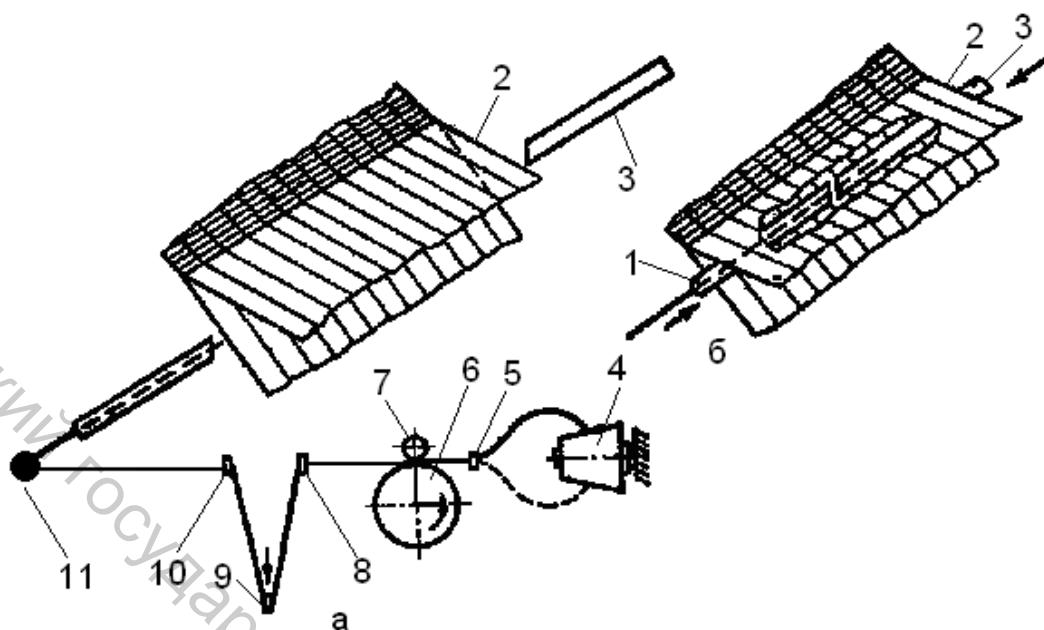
Схема прокладывания уточной нити на станке АТПР-120
